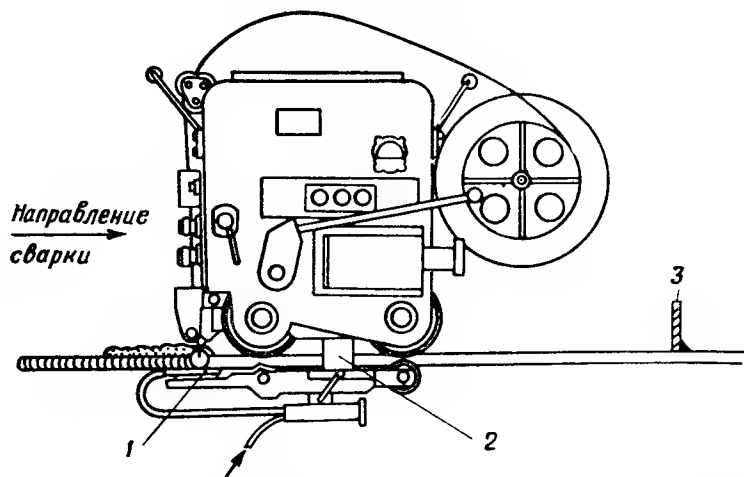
Сварочный трактор ТС-32 Института электросварки им. Е. О. Патона
